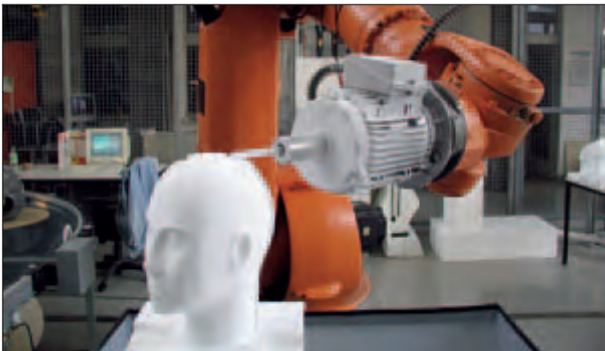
Der Kuka KR 125 Roboter mit Raspelfräser fräst eine im CAD entwickelte Figur aus Styropor. Nach der Schruppbearbeitung sieht man im Bild den Schlichtvorgang, der aus ca. 100 000 Verfahrenweisungen besteht.
